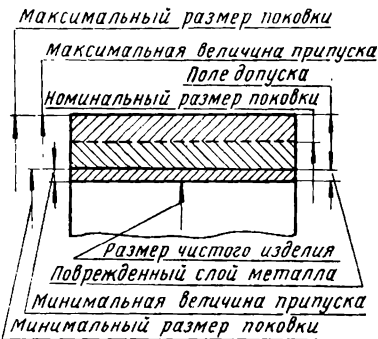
Схема размеров поковки с припусками и допусками
